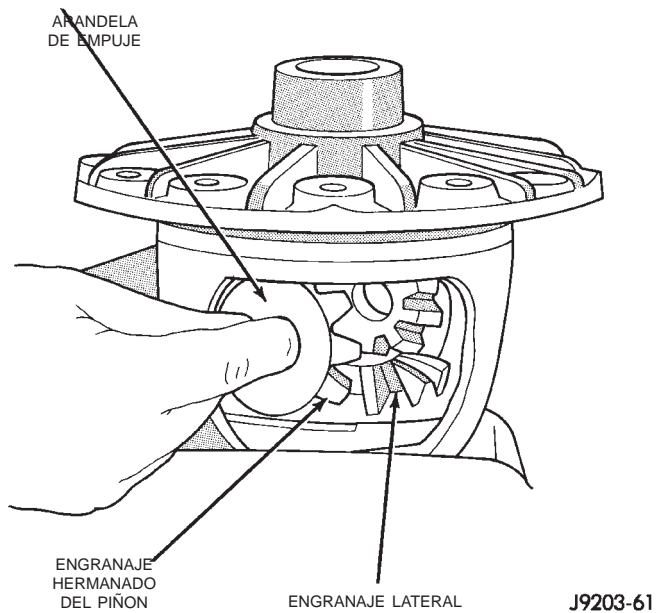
Desmontaje de los engranajes hermanados del piñón
